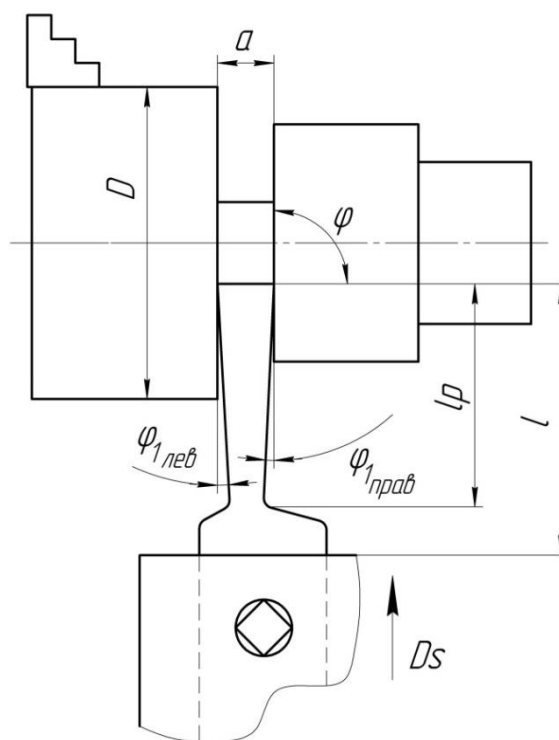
Схема отрезки резцом с головкой, оттянутой влево
